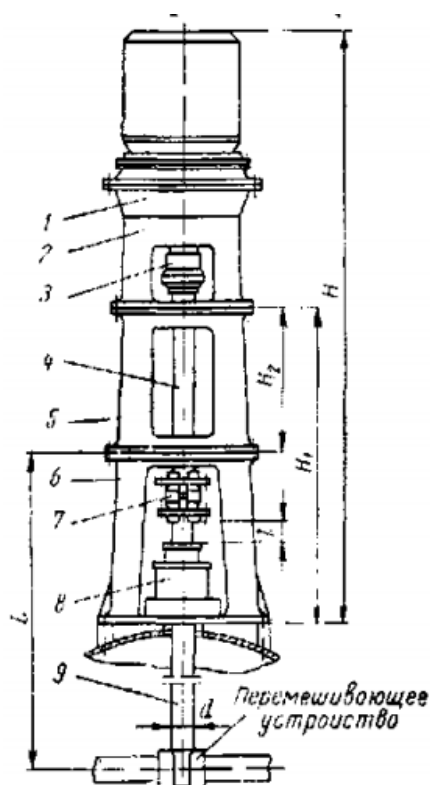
«Привод МП-560-250-3-380В-Х18Н10Т»: 1 – мотор-редуктор; 2- переходник; 3-муфта; 4-вал промежуточный; 5-стойка; 6 – стойка; 8-уплотнение; 9-вал перемешивающего устройства.
